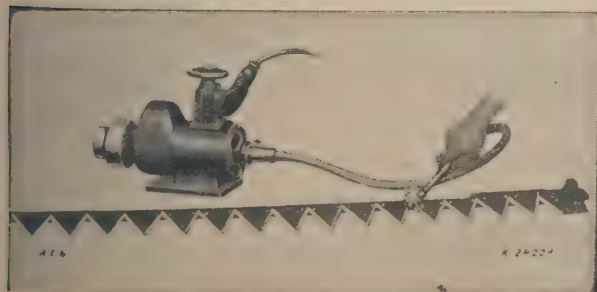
Schleifvorrichtung für Mähmaschinenmesser.
